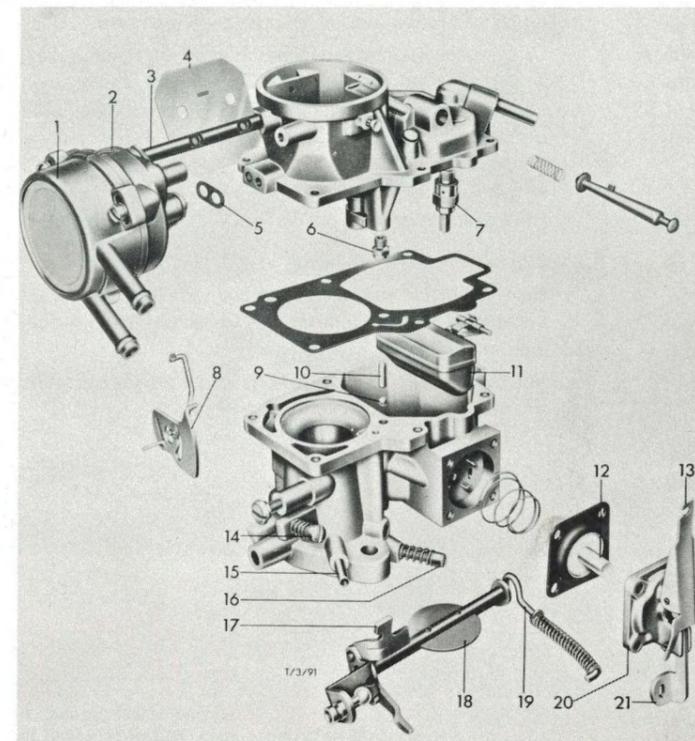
Motorcraft Vergaser V4-Motor LC-Ausführung mit Bypass-Leerlaufsystem
